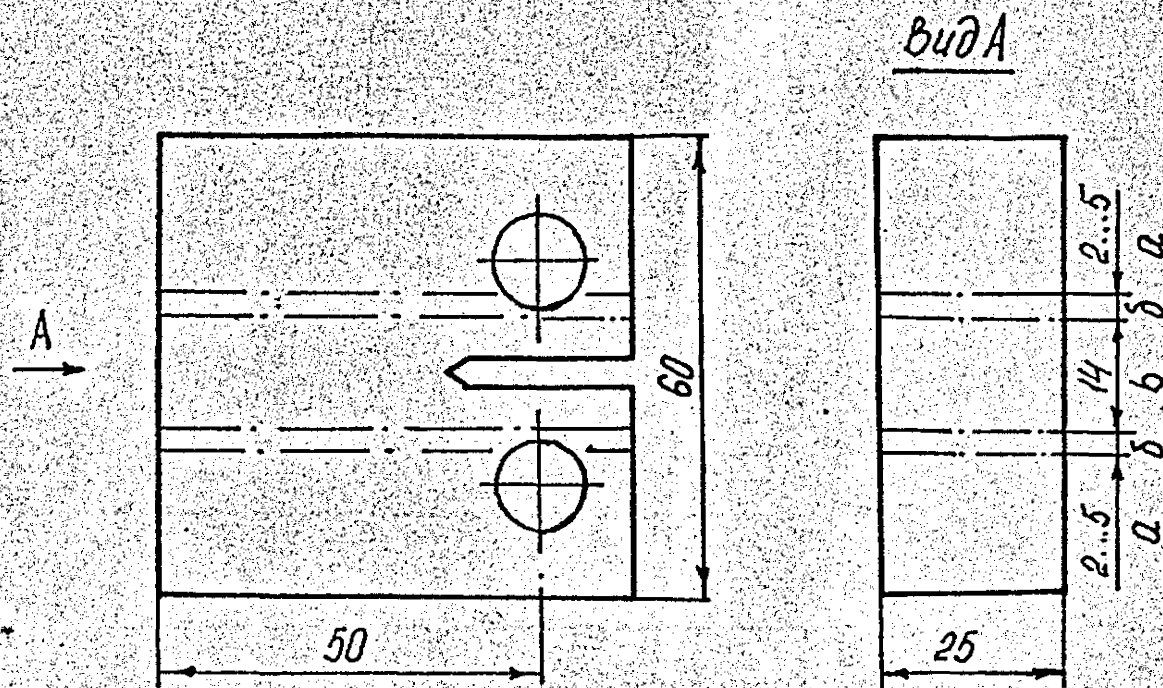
Образец для испытания на трещиностойкость металла сварного шва сплава ВТ6С. а – основной металл; б – зона термического влияния; в – сварной шов.
